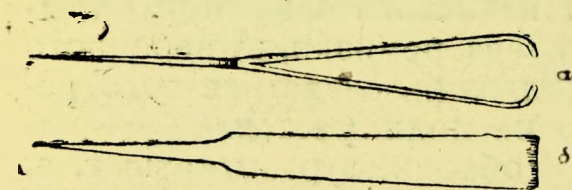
Щипчики для чистки ткани: а — вид сверху, б — вид сбоку.
